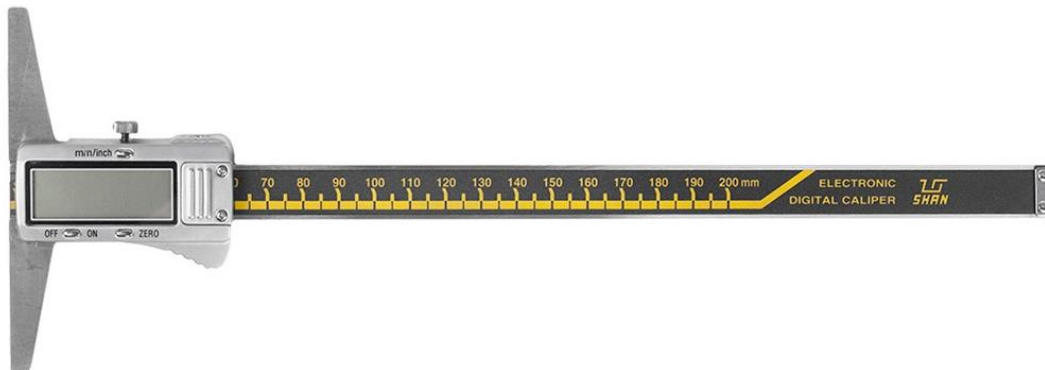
Общий вид штангенглубиномеров ШГЦ с прямой штангой
